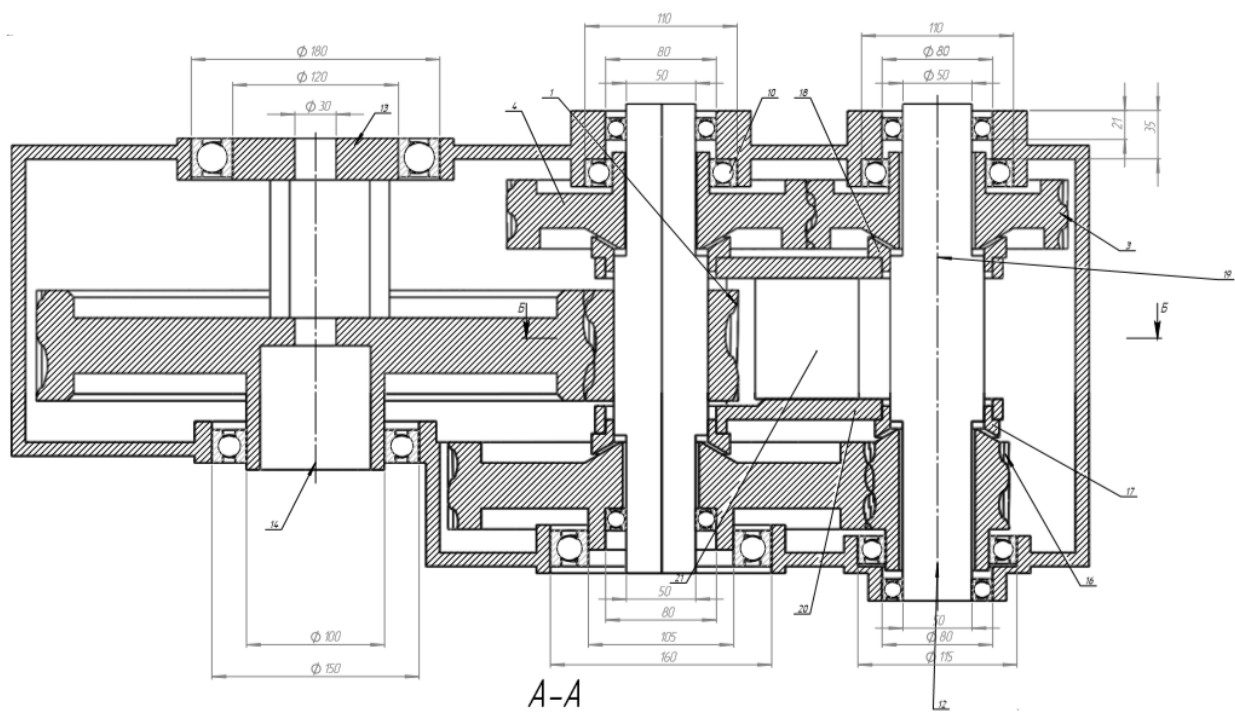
Загальний вигляд заднього редуктора(Розріз А-А).
